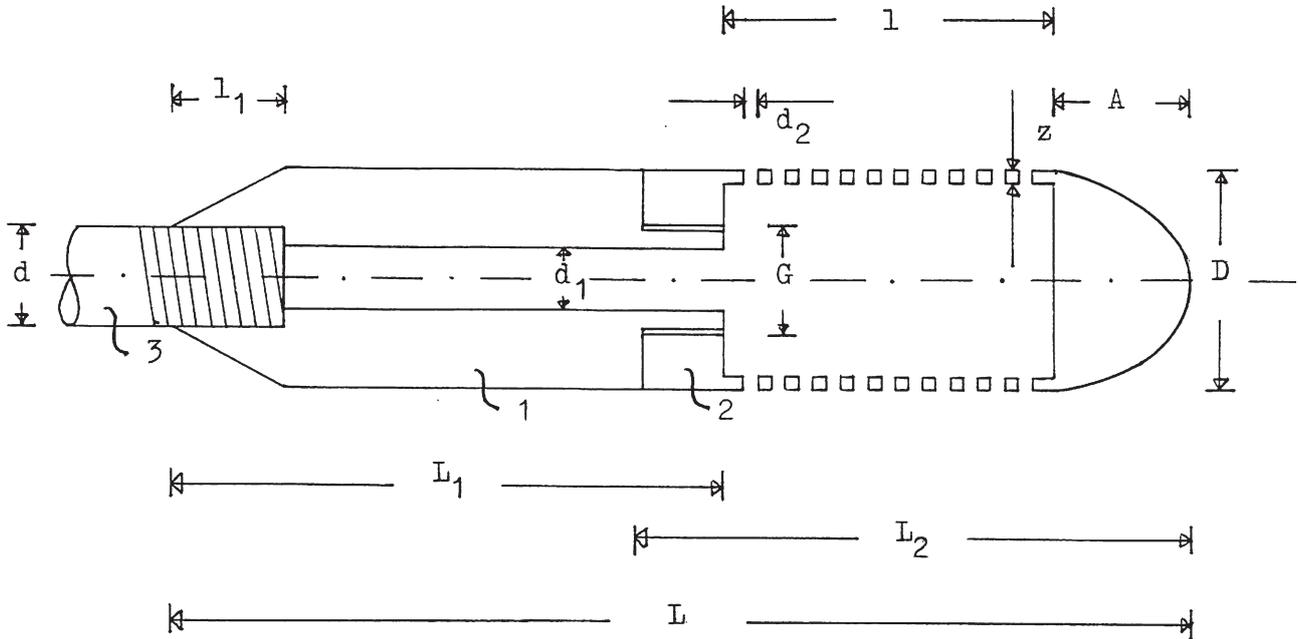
Sondenkopf. 1 Gewichtsstück, 2 Filterstück, 3 Zugfederspirale
